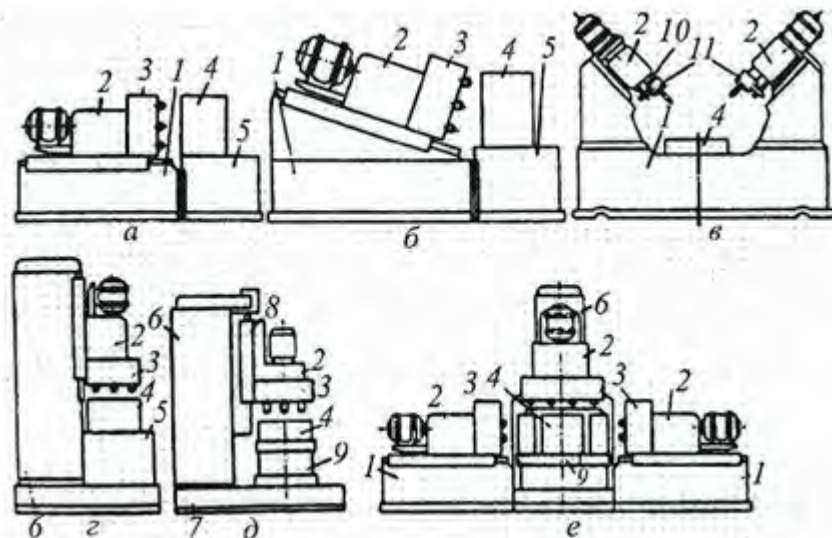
Схеми компоновок агрегатних свердлильних верстатів
